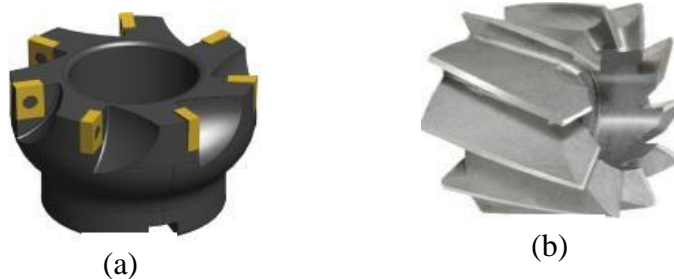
Types de fraise, a) à plaquette en carbure amovibles, b) en acier rapide (ARS).
